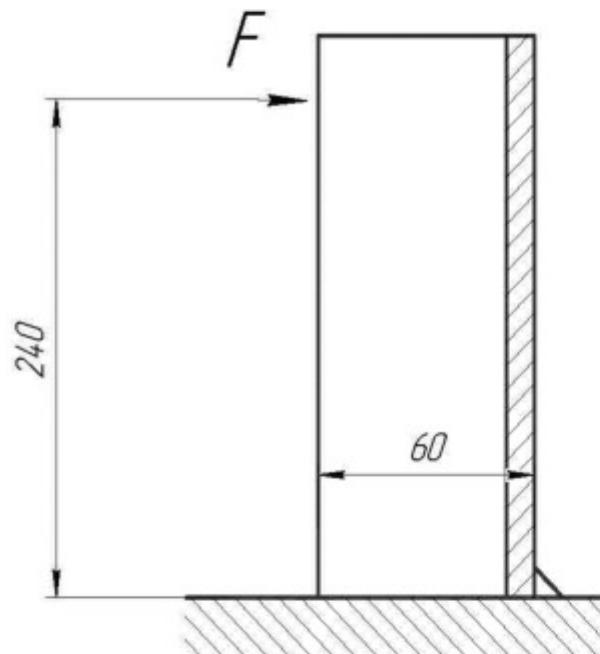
Схема нагружения сварного шва.
